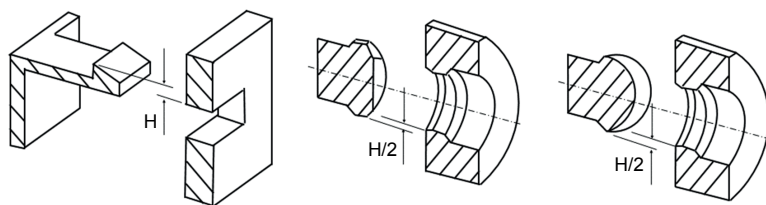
Základní typy integrovaných spojů dle geometrického hlediska
